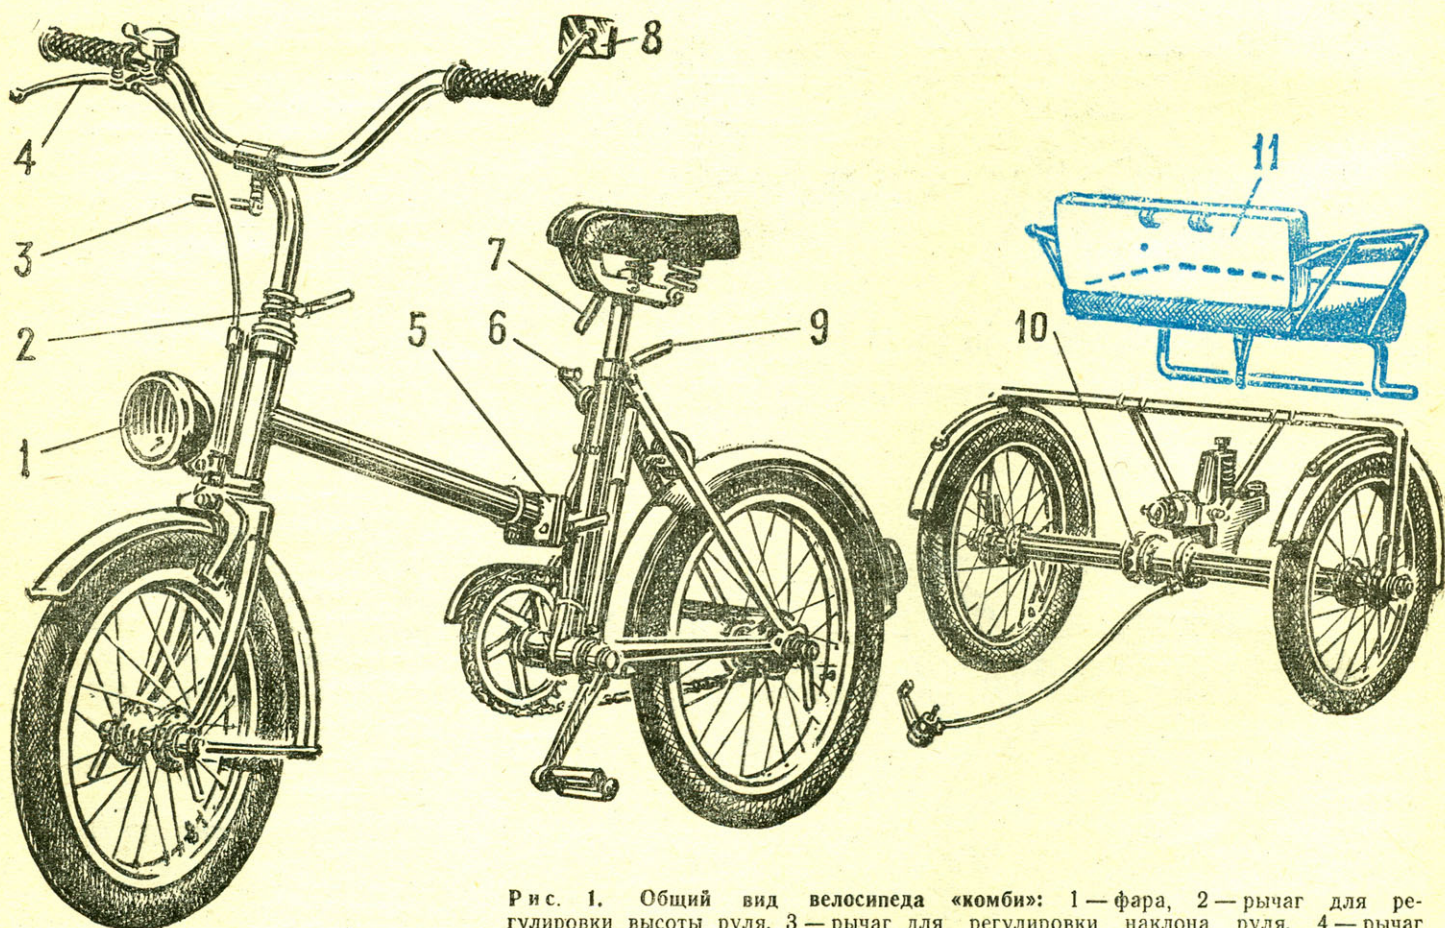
Общий вид велосипеда «комби»: 1 — фара, 2 — рычаг для регулировки высоты руля, 3 — рычаг для регулировки наклона руля, 4 — рычаг ручного тормоза, 5 — узел разъема рамы, 6 — рычаг стопора заднего моста, 7 — рычаг регулировки наклона седла, 8 — зеркало заднего вида, 9 — рычаг регулировки высоты седла, 10 — задний мост в сборе, 11 — диванчик для перевозки ребенка.
